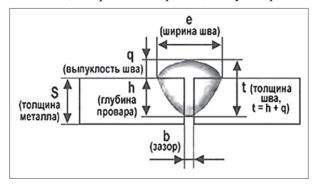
Схема сварки заготовок из алюминиевых сплавов
